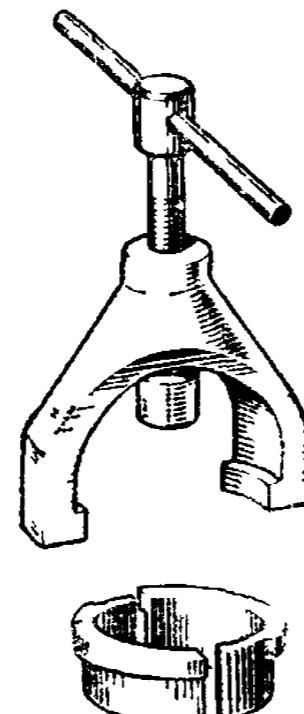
Снимание подшипника с шейки задней шапки коленчатого вала
